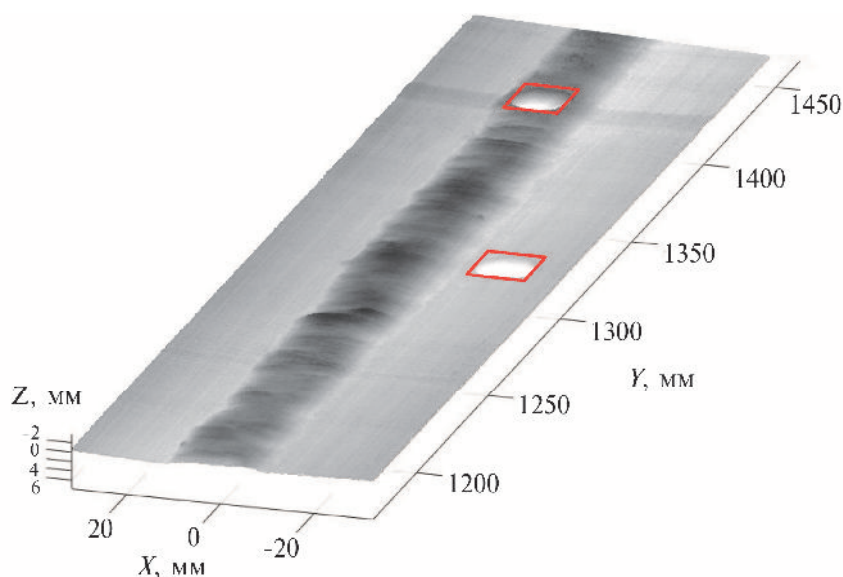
Трехмерное изображение профиля поверхности участка кольцевого СС с двумя сверлениями
